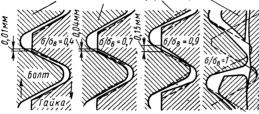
Деформации витков болта и гайки при ступенчатой нагрузке вплоть до разрушения (штриховыми линиями показан первоначальный профиль резьбы, стрелкой — направление действия нагрузки); резьба М16, материал болта и гайки — сталь 35
